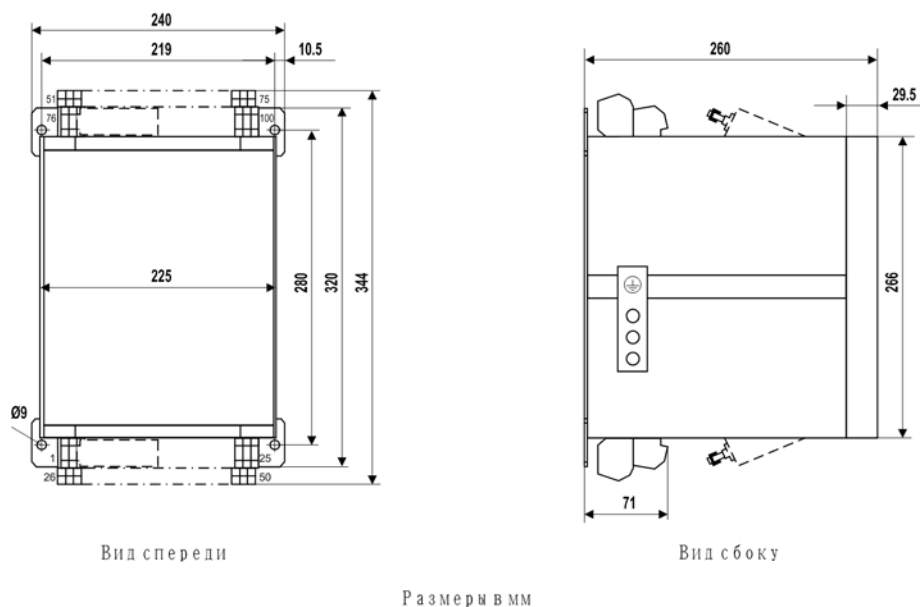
Размеры терминала 7UT613 в корпусе для навесного монтажа (размер корпуса 1/2)
